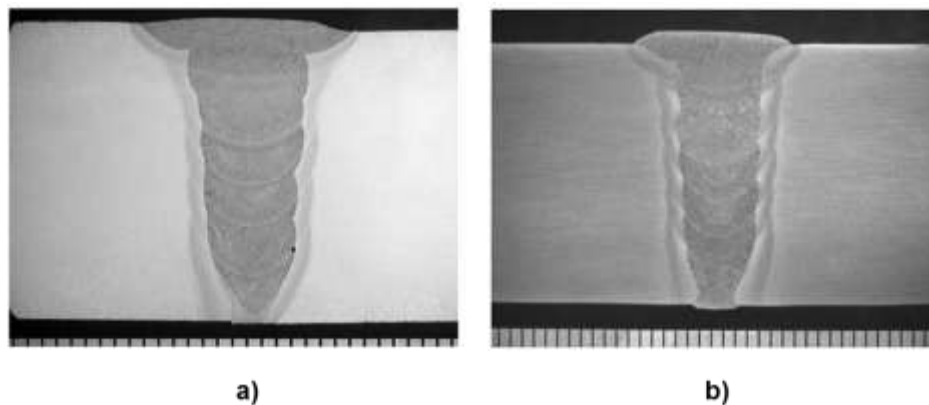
a) Macrográficas del perfil de soldaduras para las muestras de tubos de 16 pulgadas de diámetro de acero X70, con 7 pasos de soldadura, y b) soldadura en tubo de 20 pulgadas de diámetro con 8 pasos de soldadura (38).
